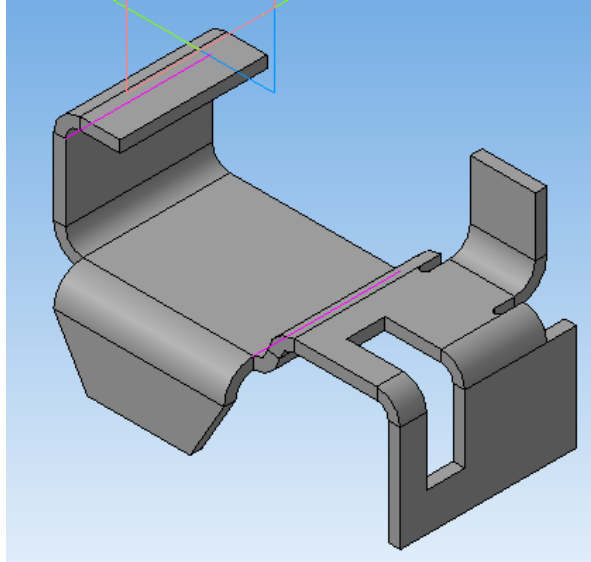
Креслення 3D-моделі листової деталі
